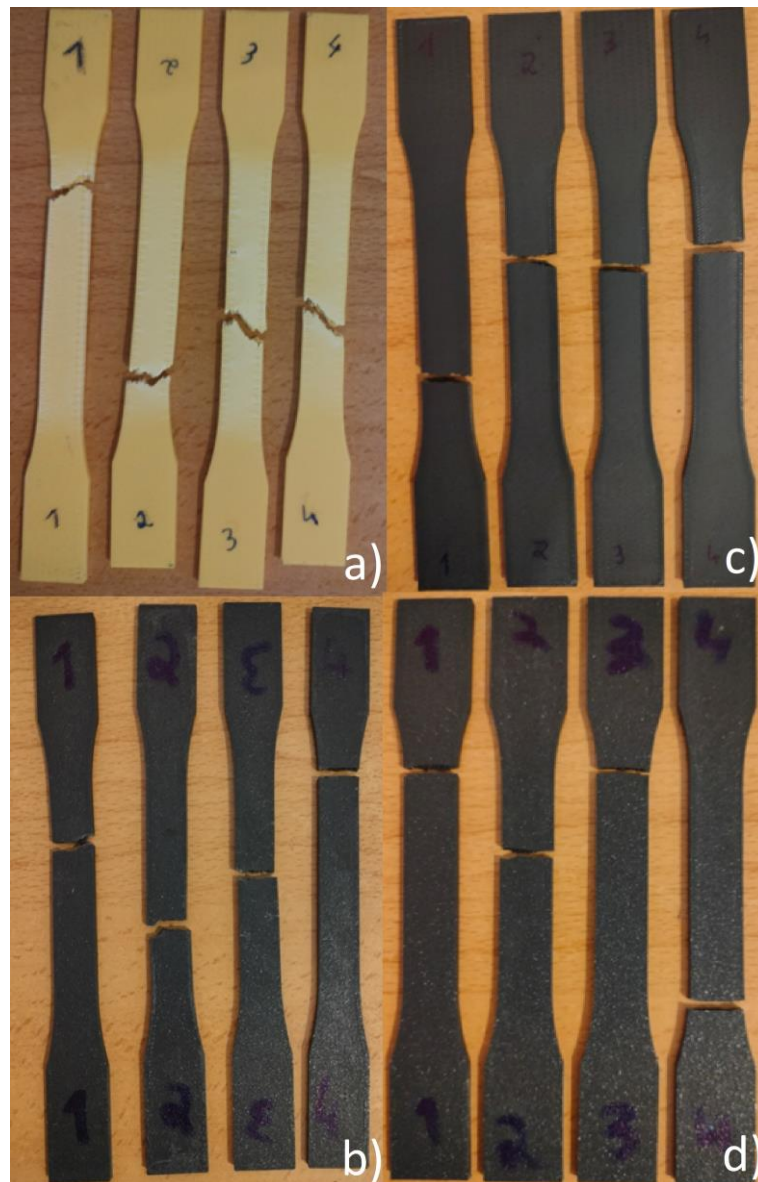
a) Provetes de PLA novo após ensaio; b) Provetes de PLA reciclado impresso a 220°C, após ensaio; c) Provetes de PLA reciclado impresso a 237°C, após ensaio; d) Provetes de PLA reciclado impresso a 255°C, após ensaio
